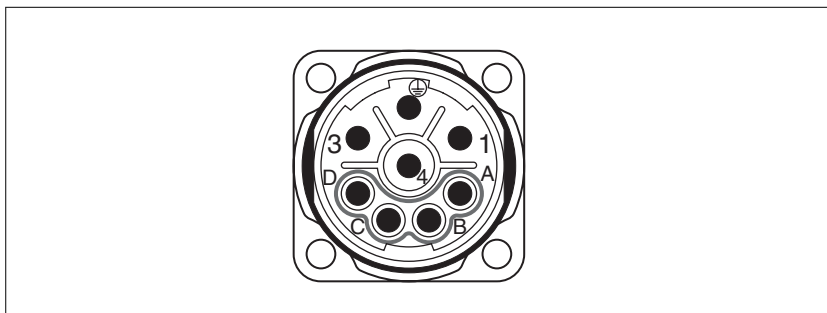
Assegnazione pin attacco di collegamento motore M23
